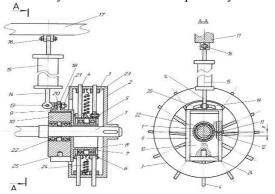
Движитель сельскохозяйственного агрегата: а) вид сбоку; б) разрез A-A;
